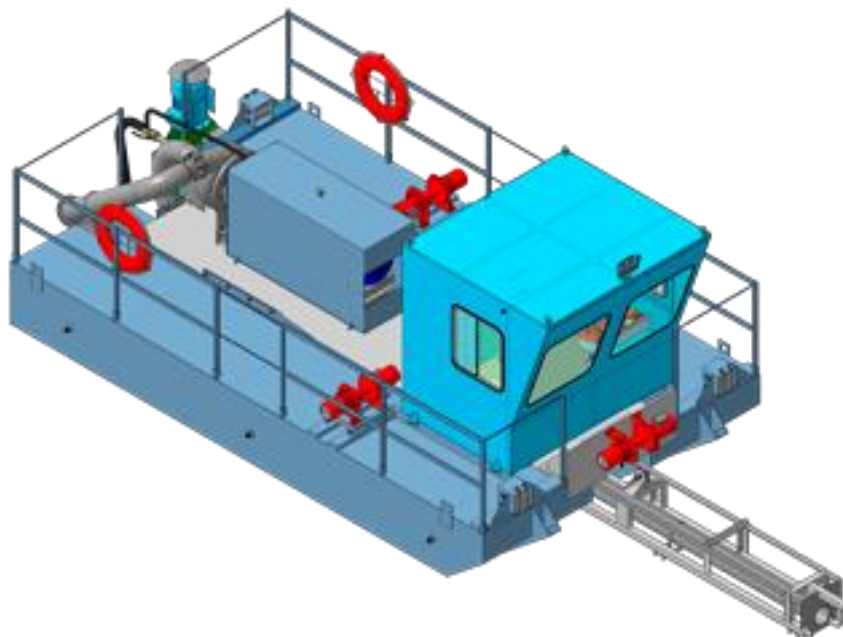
Земснаряд «Д-110/47-И-Ф» фрезерный
